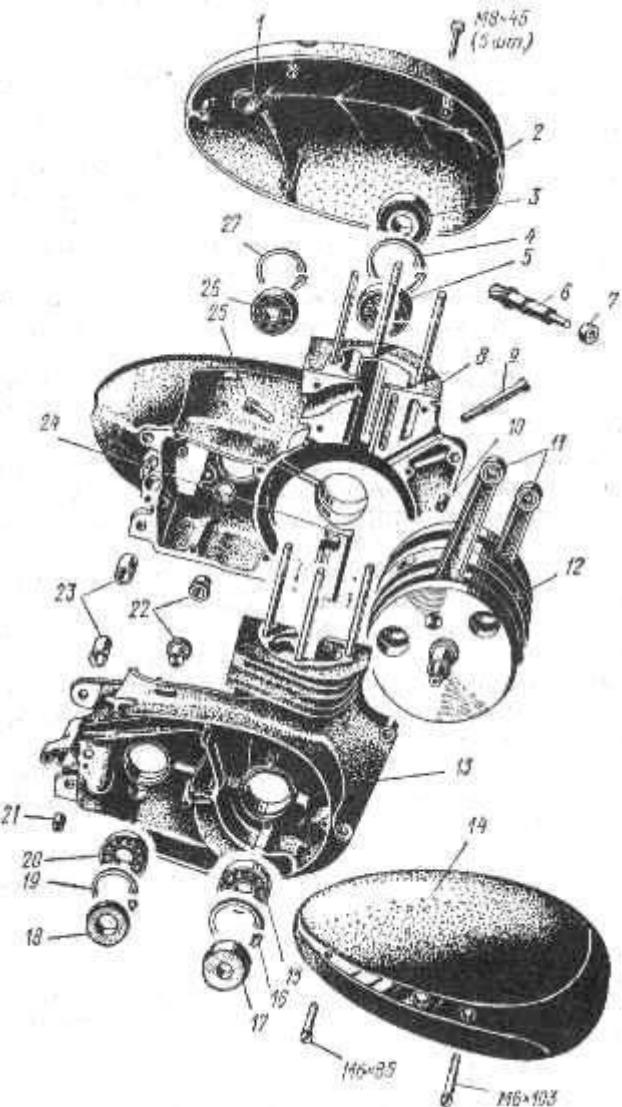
Подшипники, сальники и другие детали картера силового агрегата "Ява-350" модели 354/04:
